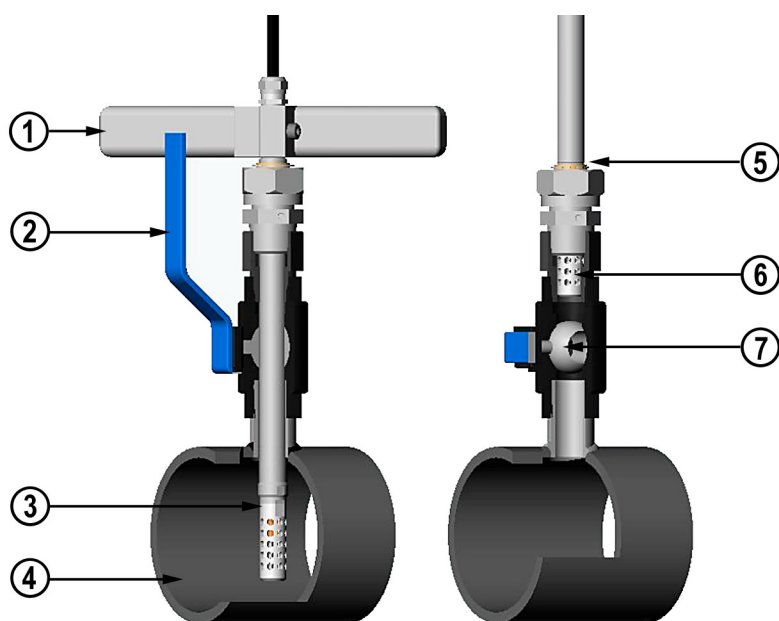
Установка датчика НМР368 через шаровой клапан в сборе
